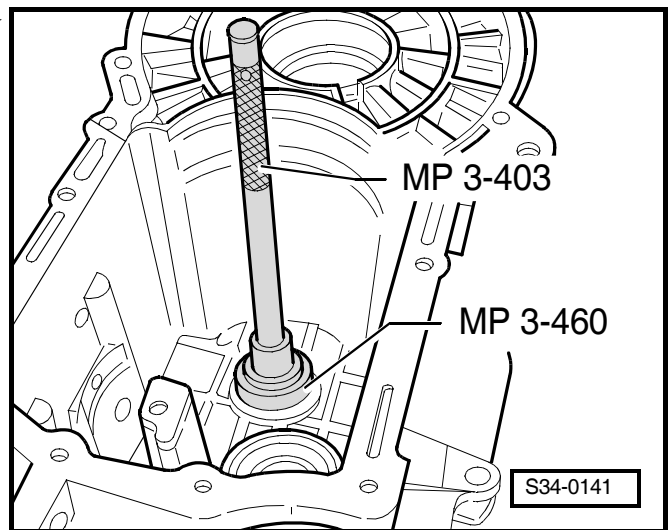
Chasser la bague d'étanchéité de la douille de guidage
